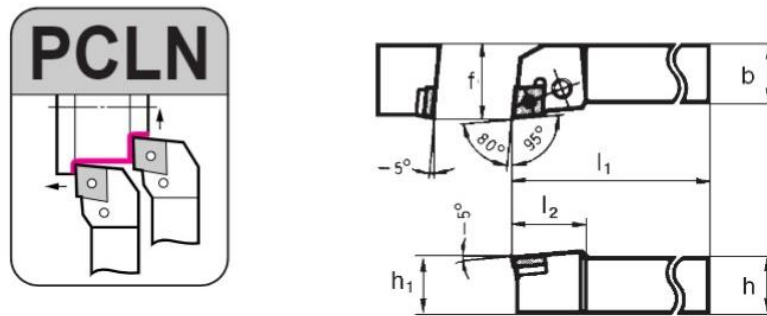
Державка PCLN R 2525 M19 [1, с. 122]
